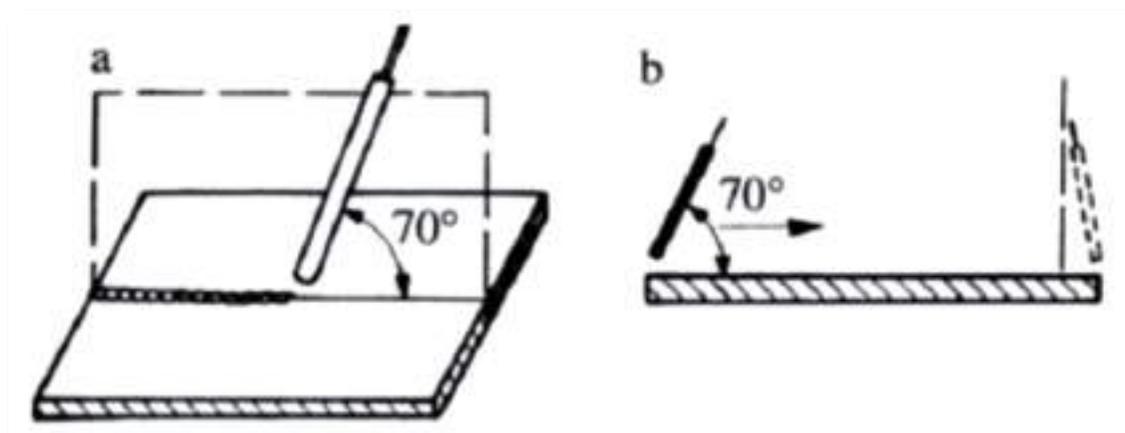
Posição do elédrodo na soldadura ao baixo.
